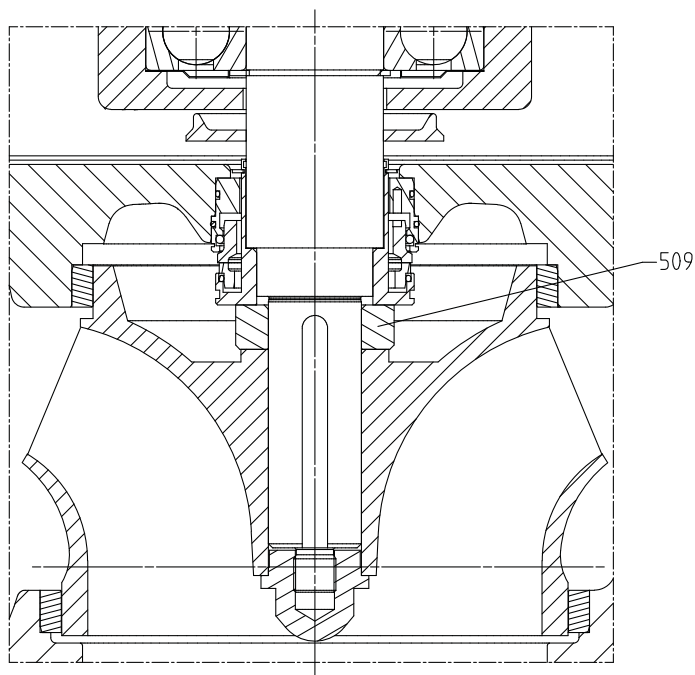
Ausführung mit Zwischenring (nur bei Baugröße 250-250, 250-300, 350-340)
